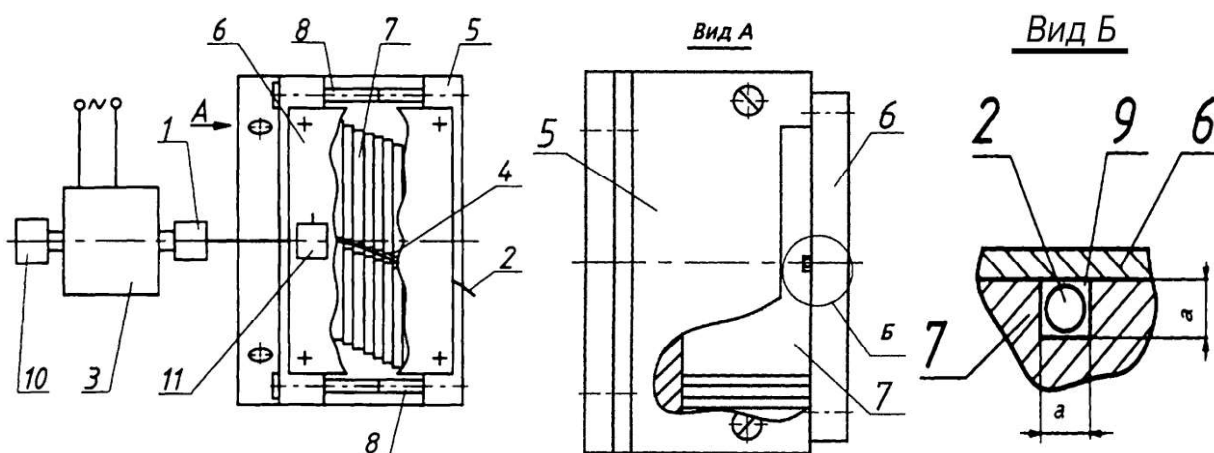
Общая схема установки для усталостных испытаний тонких проволок, где 1- патрон для закрепления проволочного образца; 2 - проволочный образец; 3 - привод для вращения патрона и устройство для создания в образце изгибной нагрузки; 4 - криволинейный канал; 5 - поля обойма; 6 – крышка; 7- набор пластин; 8 - узлы фиксации; 9 – пазы; 10 - датчик для контроля числа оборотов привода вращения патрона; 11- датчиком для регистрации факта разрушения проволочного образца
